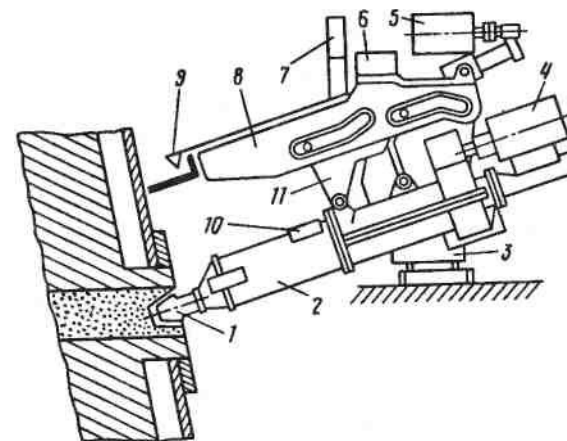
Электрическая пушка для забивки летки: 1 — носок; 2 — цилиндр; 3 — колонна; 4 — механизм,двигающий поршень; 5 — механизм движения тележки; 6 — механизм поворота пушки; 7 — привод; 8 — лафет; 9 — защелка; 10 — люк; 11 — тележка
